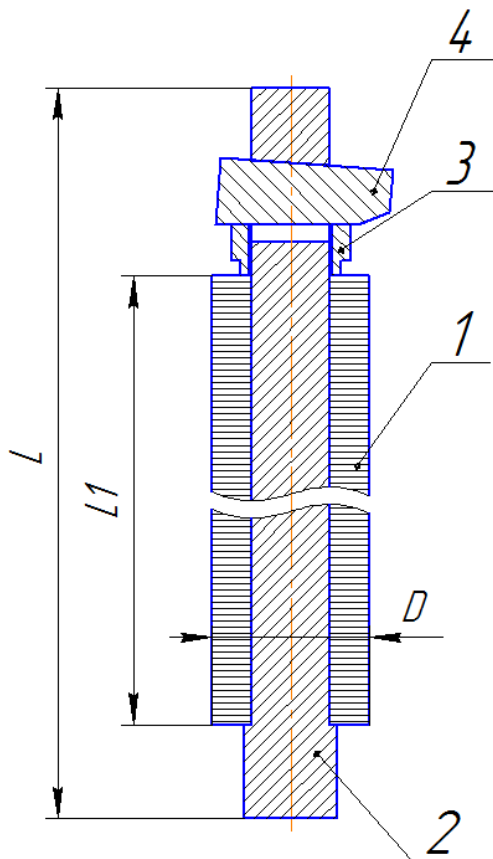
Конструкция пакета ротора (с оправкой)
